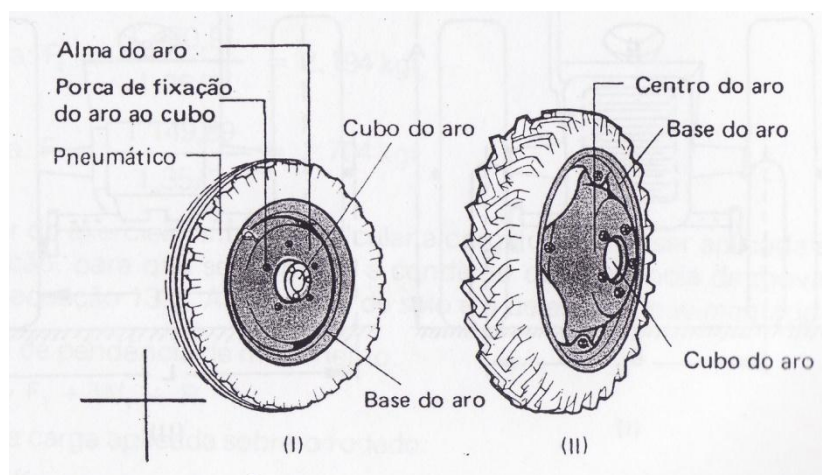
Composição do rodado pneumático: roda frontal de direção (I); roda traseira motriz (II)
